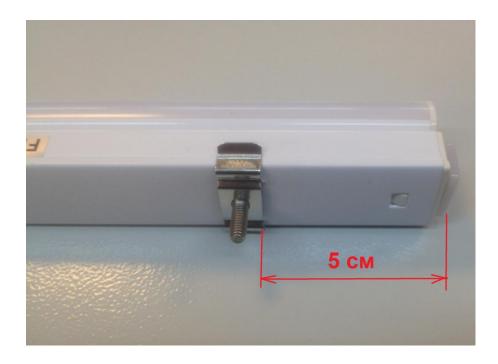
Установка крайнего пружинного держателя.
